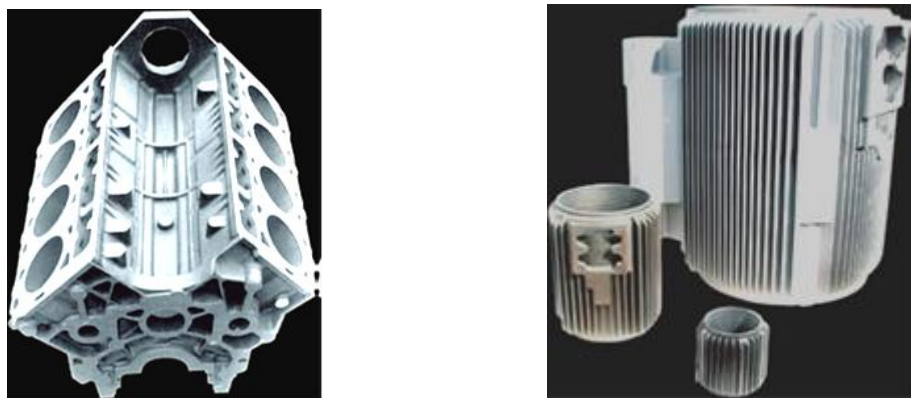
Отливка блока двигателя и корпуса электродвигателей, отлитые по формам, изготовленным с помощью воздушного потока с последующим прессованием.
